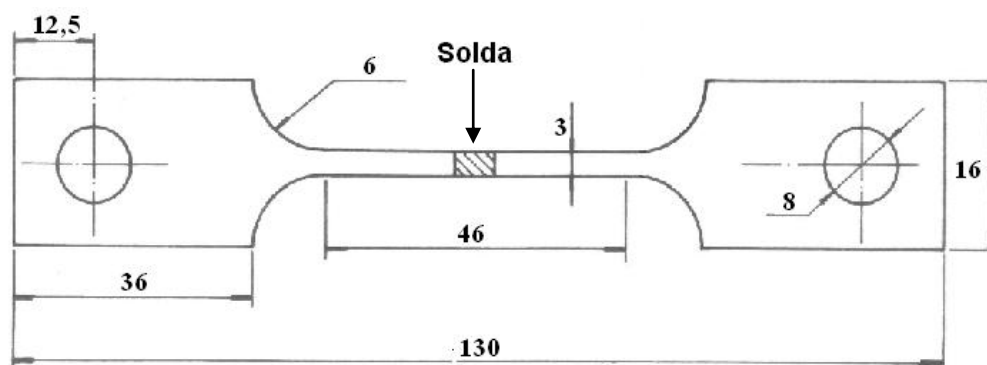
Geometria e dimensões do Corpo de prova CST (dimensões em mm)
